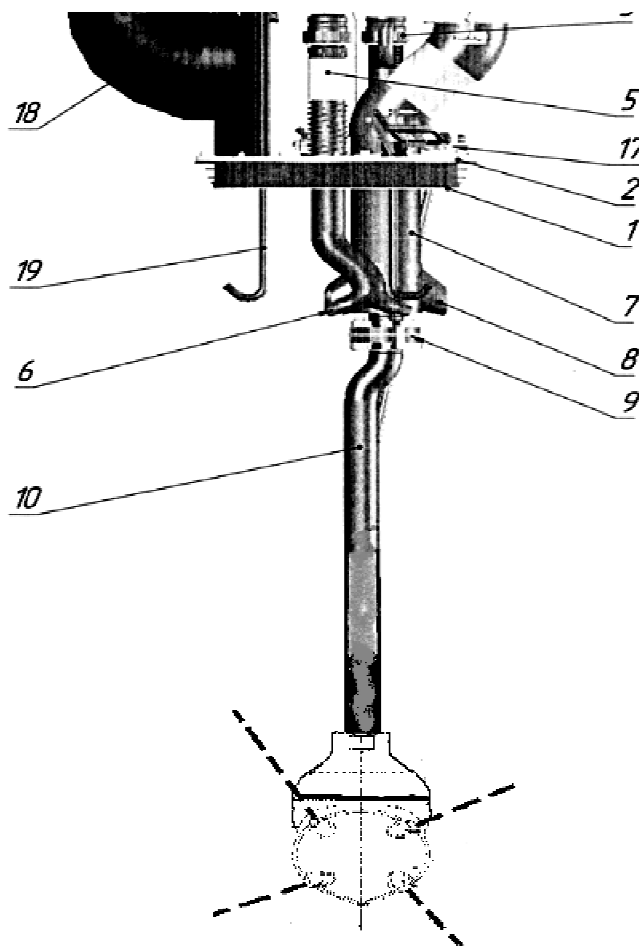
Мийна установка з ротаційною форсункою
